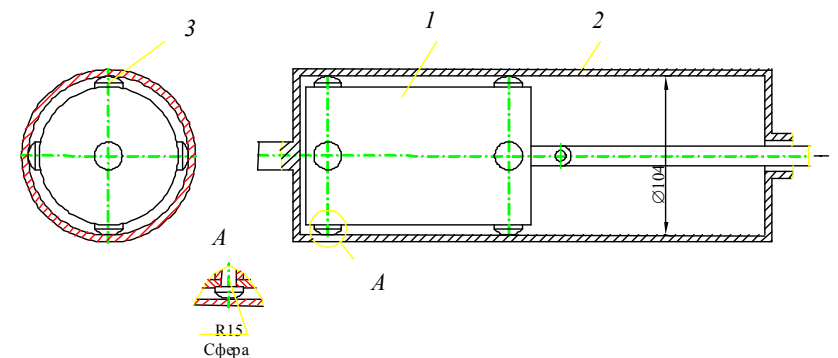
Стержень в корпусе: 1 – стержень; 2 – корпус; 3 – упор
